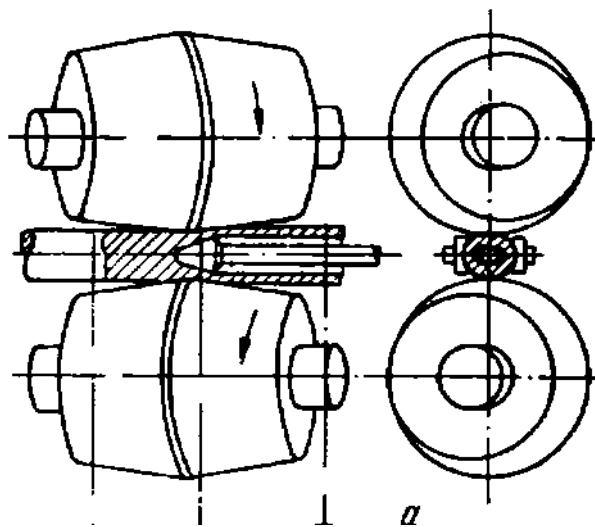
Схема прошивки заготовок в двухвалковых станах винтовой прокатки.
